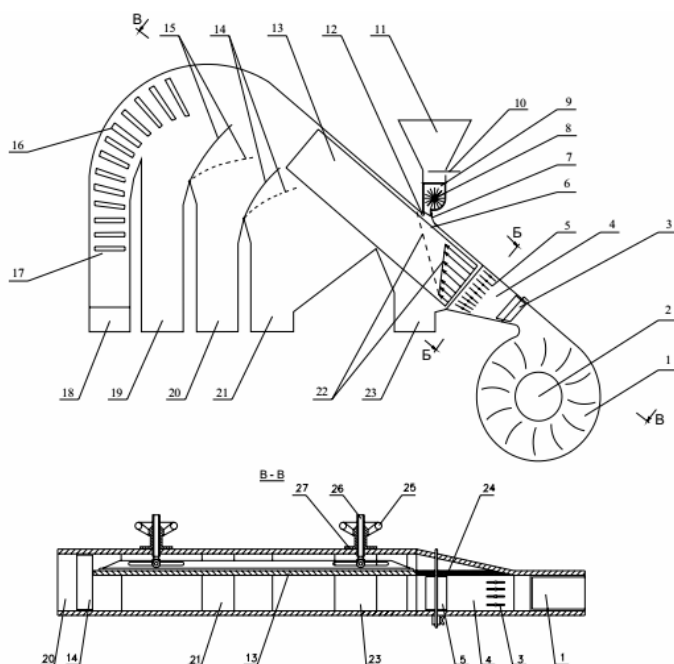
Схема пневматичного сепаратора з нахиленим повітряним каналом: 1 – вентилятор; 2 – патрубок вхідний вентилятора; 3 – жалюзі вертикальні; 4 – проставка; 5 – пластини поворотні; 6 – камера сепарувальна; 7, 12 – патрубки; 8 – щітка циліндрична; 9 – боковина рухома; 10 – заслінка регульовальна; 11 – бункер; 13 – подільник; 14, 15 – перегородки; 16 – інерційний пиловідокремлювач; 17 – пилоосаджувальна камера; 18 – фільтр; 19 – 21, 23 – приймачі фракцій; 22 – епіюра швидкості в робочій зоні
